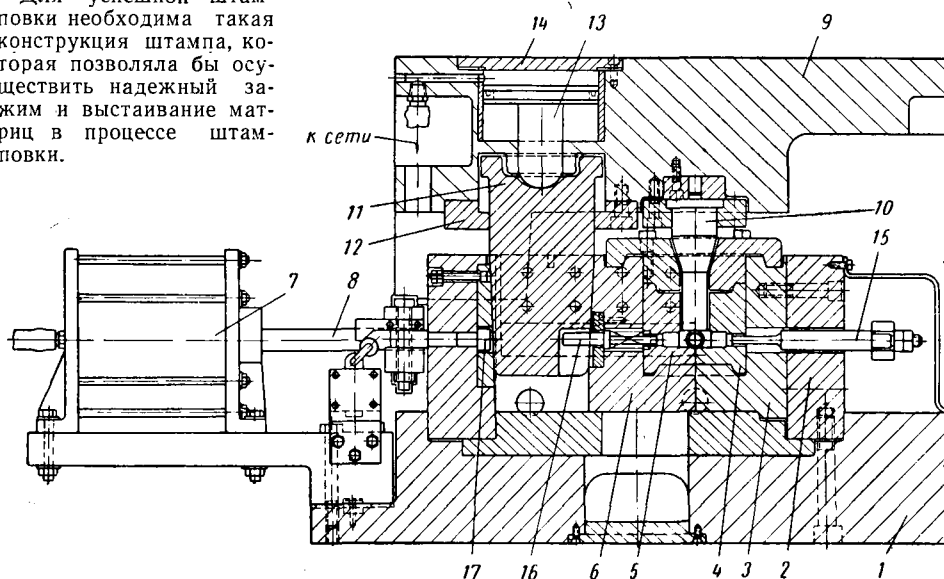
Штамп для изготовления крестовины карданного вала с вертикальным разъемом матриц.
